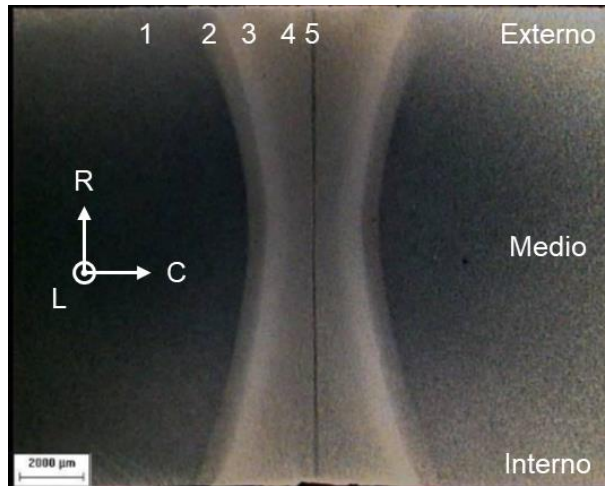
Macrografía de la soldadura del tubo de 14,8 mm de espesor antes del TTC. Las zonas asociadas a la soldadura son: (1) metal base, (2) ZAC no deformada, (3, 4) ZAC y (5) línea de soldadura [10].
